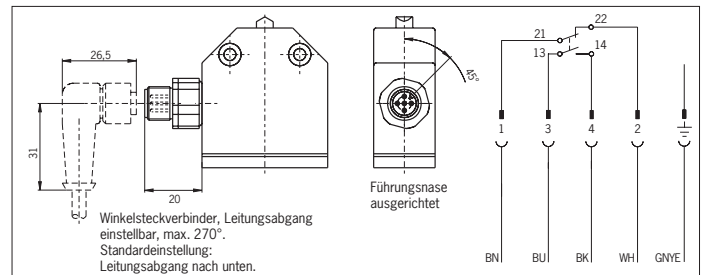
Maßzeichnung/Anschlussplan SN01.558SVM5 mit Steckverbinder M12 (SVM5, 5-polig)
